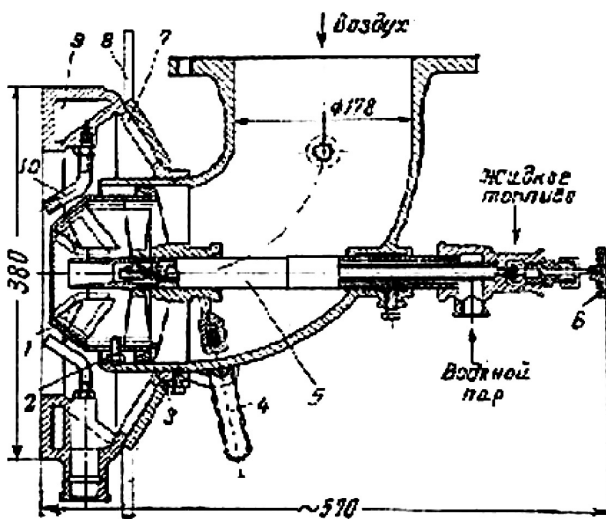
Горелки типа ФГМ: 1 — завихритель; 2 — крепление завихрителя; 3 — воздушная заслонка; 4 — рукоятка заслонки; 5 — парожидкостная камера; 6 — топливный вентиль; 7 — воздушные окна; 8 — регистр; 9 — кольцевой газовый коллектор; 10 — наконечники газового коллектора
